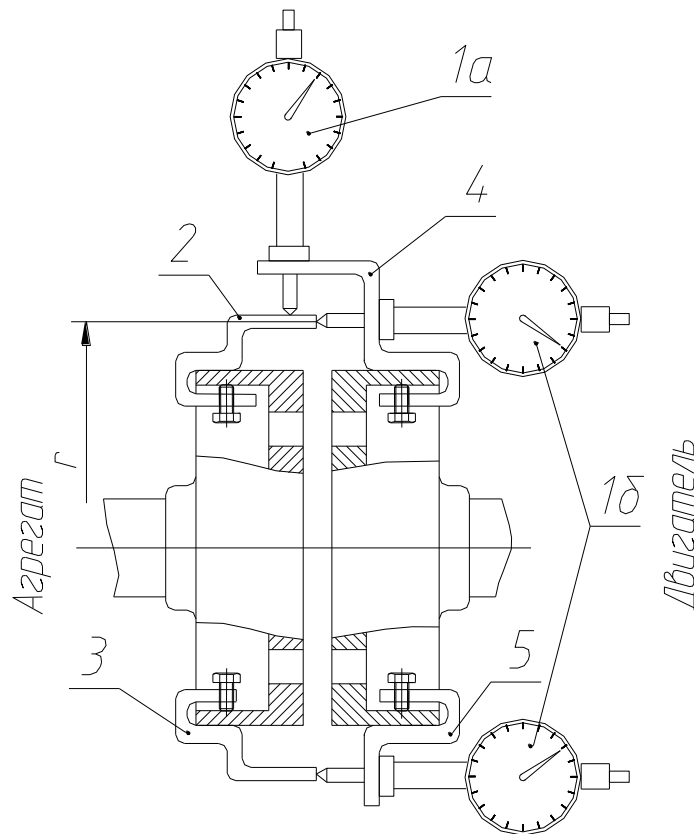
Приспособление для центровки, укрепленное на ободах полумуфт.
